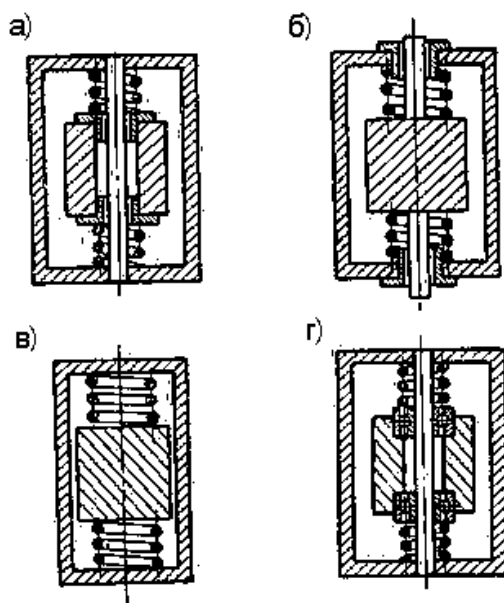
Схематическое изображение подвесов с дополнительными направляющими элементами
